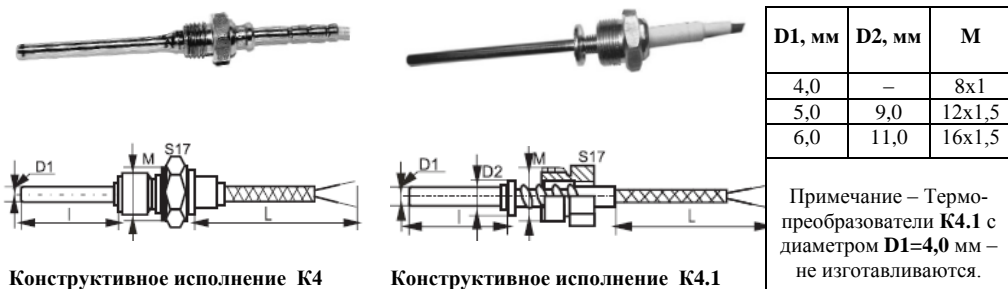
Внешний вид и габаритные размеры термопреобразователя
